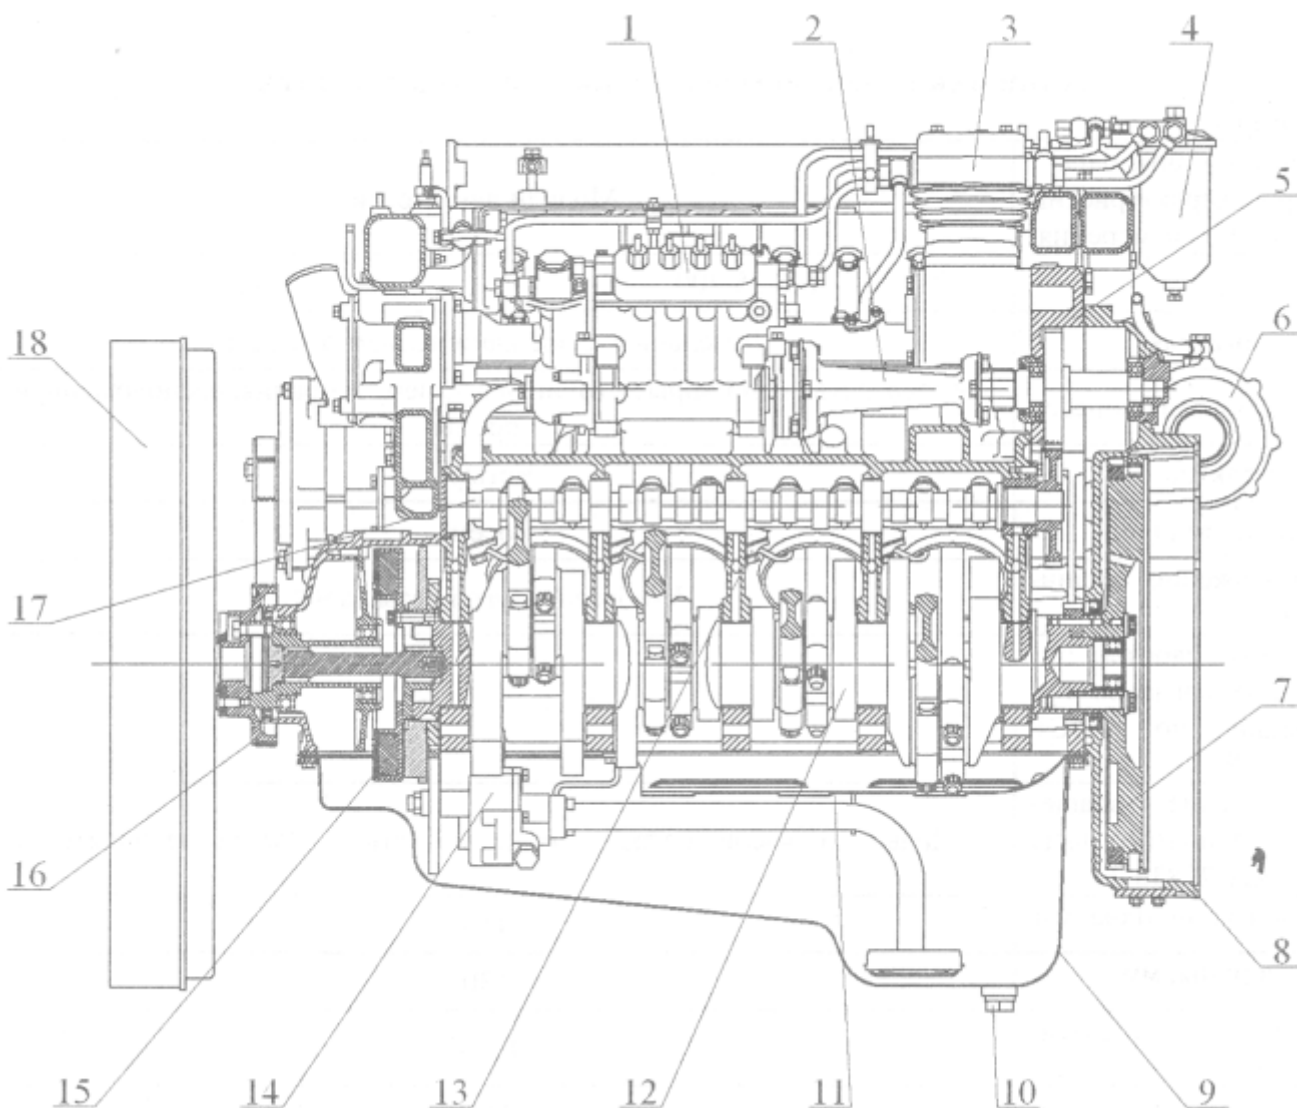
Продольный разрез двигателя с V-образным ТНВД «ЯЗДА»: 1 - топливный насос высокого давления (ТНВД); 2 - привод
